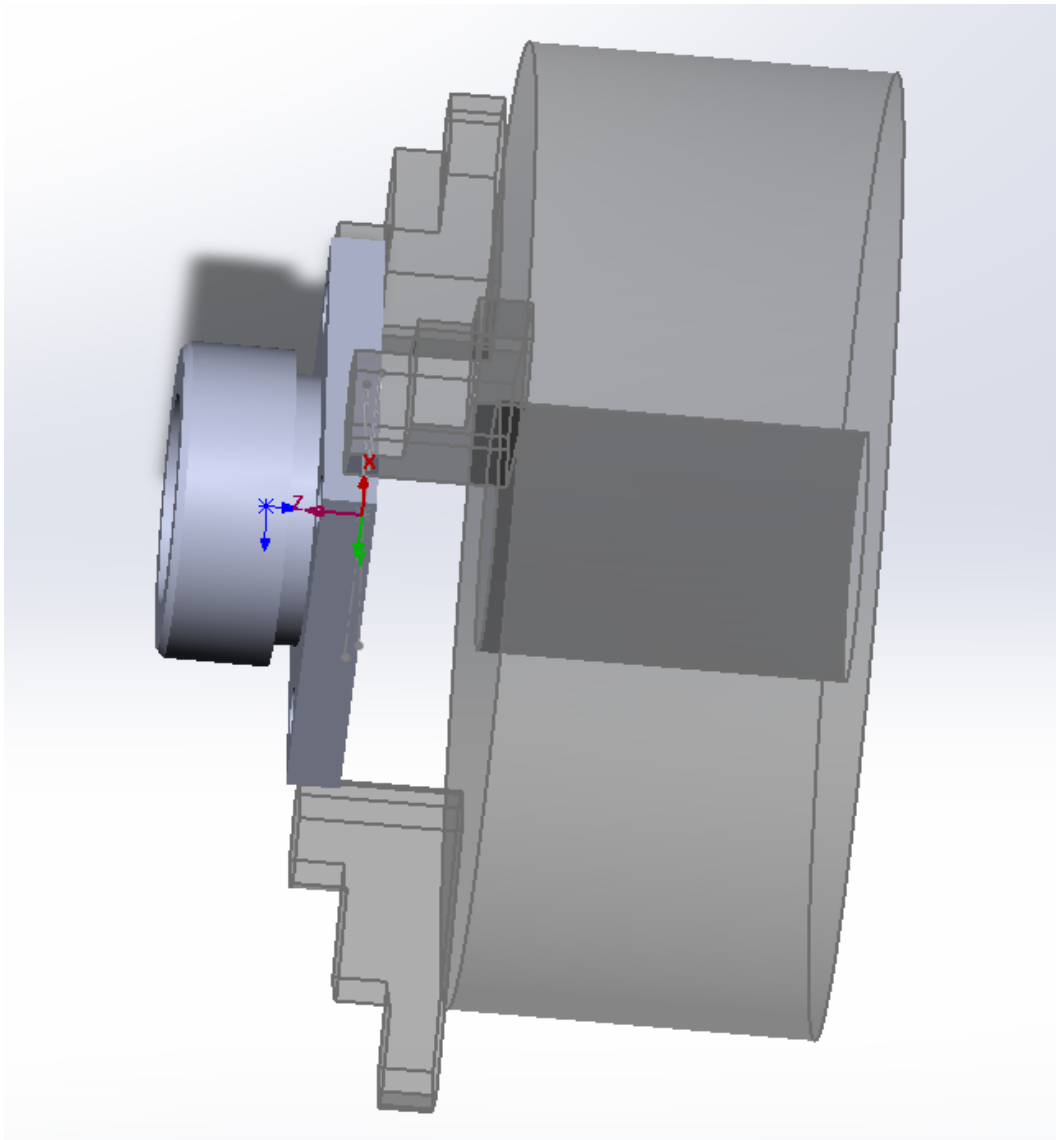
Затиск деталі в трикулачковому патроні токаного верстата з ЧПК.
